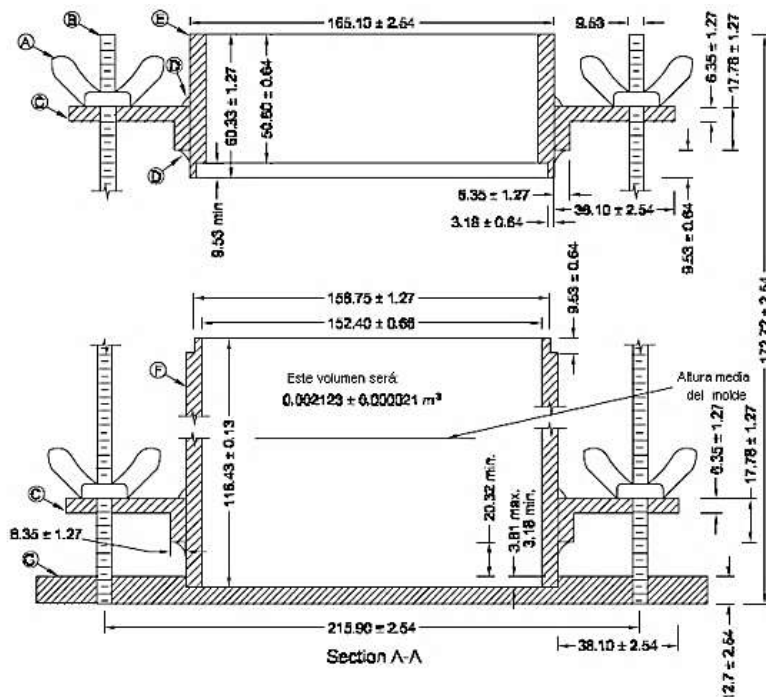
Molde cilíndrico de 152,4 mm (6 in) para el ensayo Proctor Modificado, dimensiones en mm.
